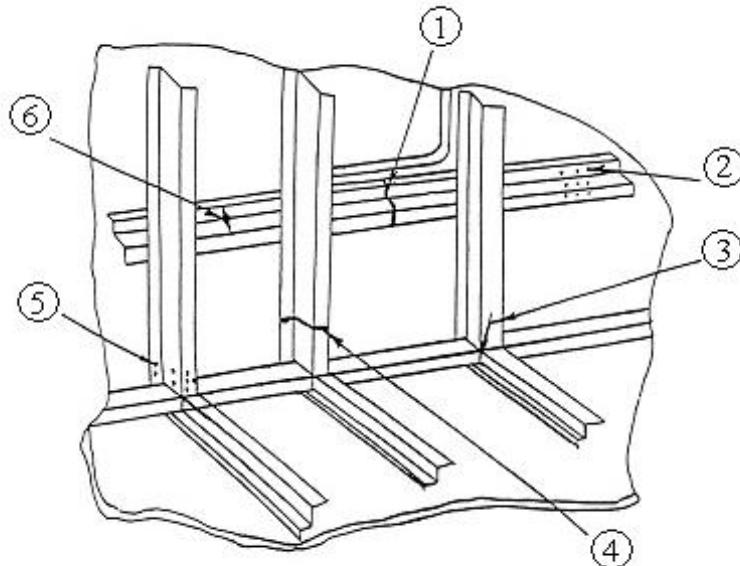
Дефекты каркаса кузова, ремонтируемые сваркой или наплавкой
